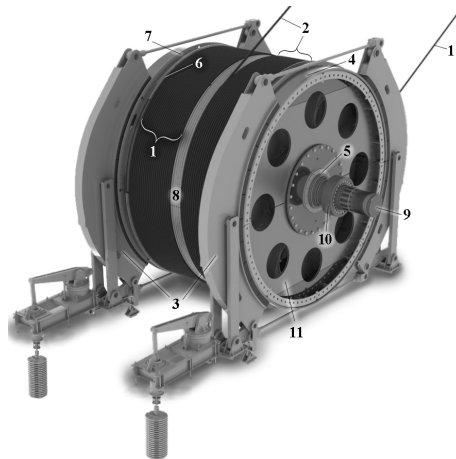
Барабан ШПМ типу ЦР з гальмами: 1 – намотуваний канат зі скіпом; 2 – змотуваний канат із противагою; 3 – гальмівні колодки; 4 – гальмівні поля; 5 – маточини; 6 – мала реборда; 7 – велика реборда; 8 – обичайка; 9 – вал; 10 – підшипники; 11 – лобовини
